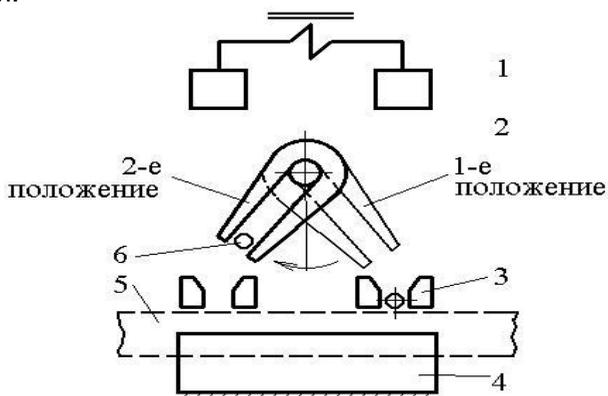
Схема укладки поперечных стержней в сварочной машине.
